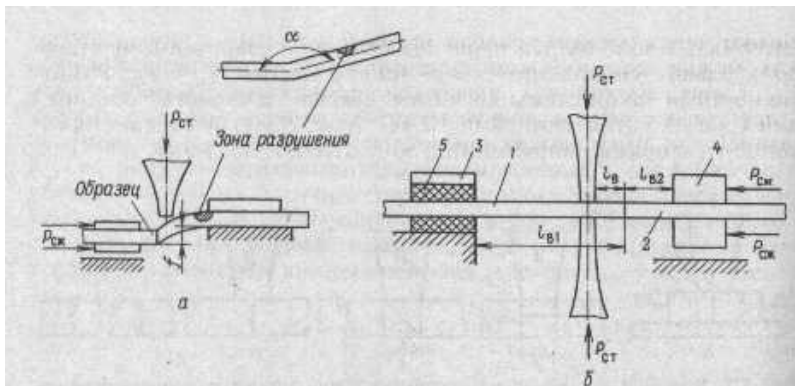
Схема стыковой ультразвуковой сварки с тангенциальным вводом колебаний: а - с относительным перемещением элементов (отдельно показано сварное соединение, полученное по такой схеме); б - с двусторонним вводом колебаний и относительным перемещением элементов; 1, 2 - образцы; 3 - неподвижный зажим; 4 - подвижный зажим; 5 - резиновая прокладка;  $l_{в1}$  и  $l_{в2}$  - длины вылета образцов;  $l_{в}$  - расстояние от боковой поверхности волновода до зоны сварки; f - прогиб образца
